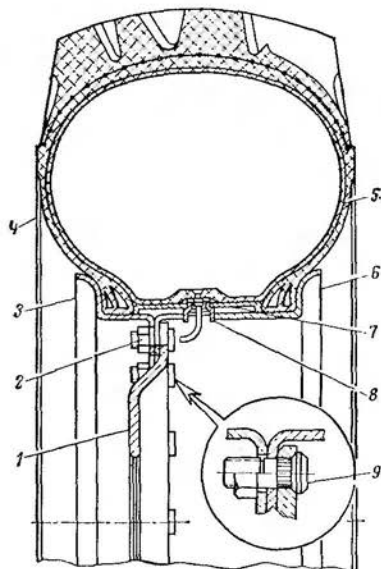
Конструкция колеса с шиной в сборе автомобиля ГАЗ-66:
